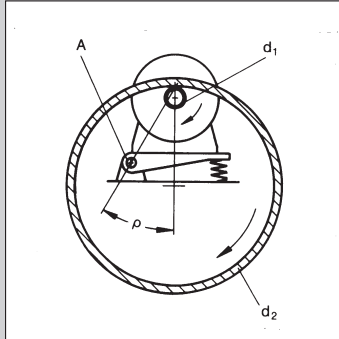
Steuerwinkel im Innen-Gummiwälzgetriebe
